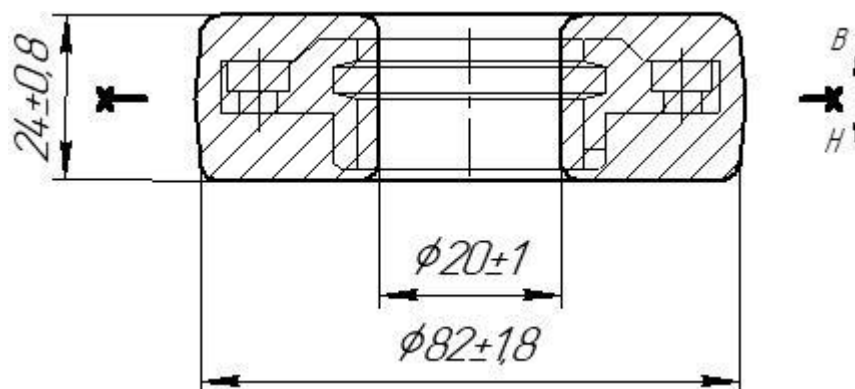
Ескіз заводської заготовки Кришки підшипника
